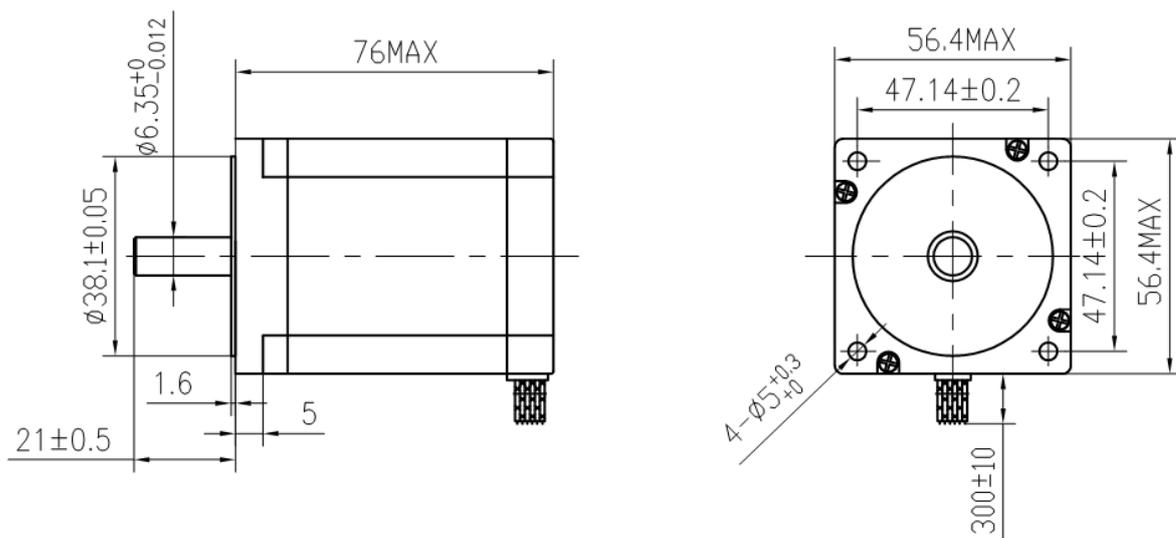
Шаговый двигатель NEMA23HS7430
